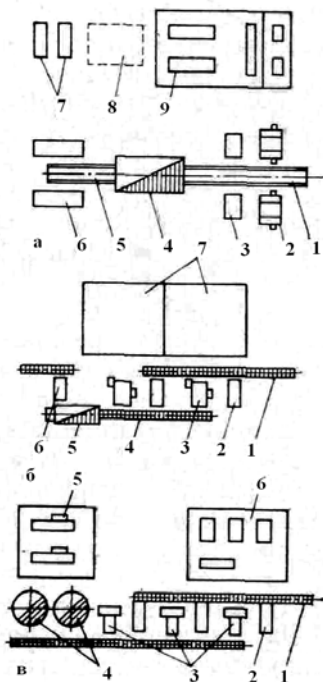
Розміщення верстатів для термічної обробки з нагріванням СВЧ у потоці механічних цехів: а – ділянка гартування шийок колінчатих валів; б – ділянка для гартування внутрішньої поверхні гільз; в – ділянка загартування зубів шестірень
